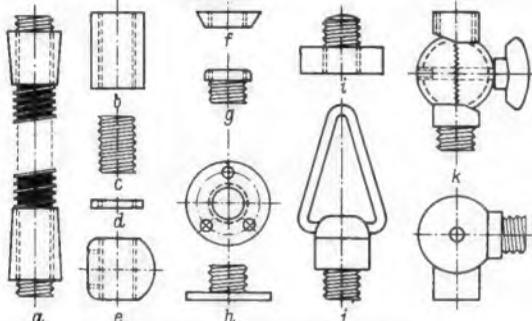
Die Einzelteile. a = flexibler Metallschlauch, b = Muffe mit Innengewinde, c = Rohrstück mit Außengewinde, d = Ringmutter, e = Kugelnippel mit Gewinde in T-Form, f = konische Mutter, g = Kunststoffnippel, h = Scheibennippel, i = Aluminium-Zwischenstück Fotoapparat - Fotostativ, j = Aufhängenippel mit Außengewinde, k = Gelenknippel
